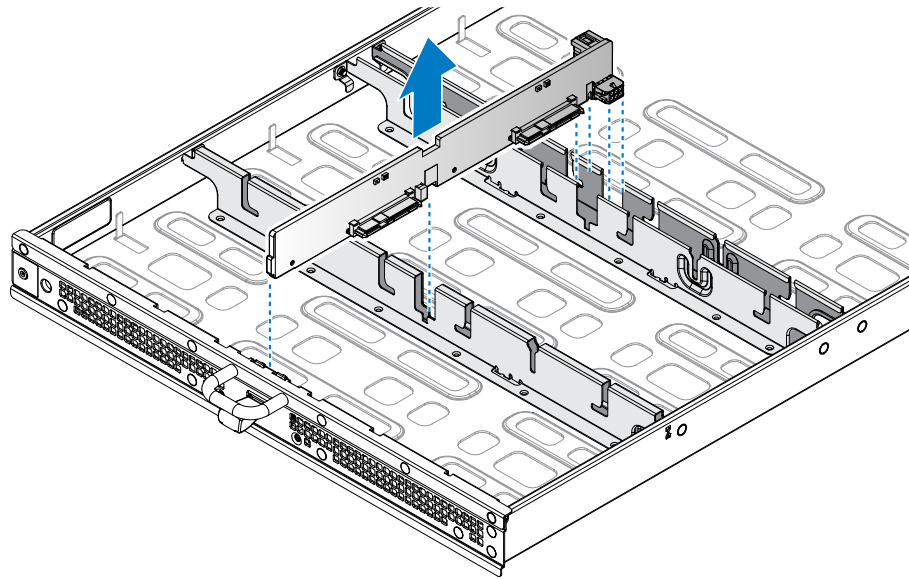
Entfernen der Festplatten-Rückwandplatine
